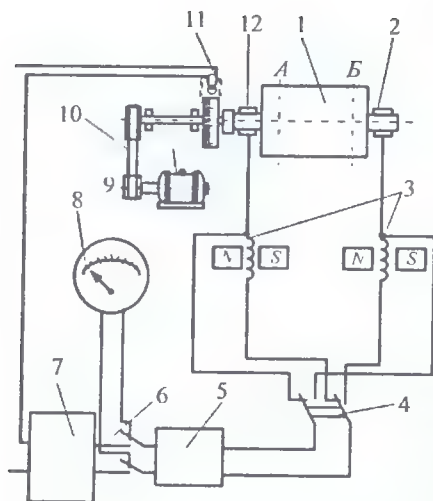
Схема станка для динамической балансировки: 1—балансируемый ротор; 2,12 — подшипники; 3—катушки; 4,6—переключатели; 5,7—усилители; 8—указатель; 9—эл. двигатель; 10—передача; 11—стробоскоп
